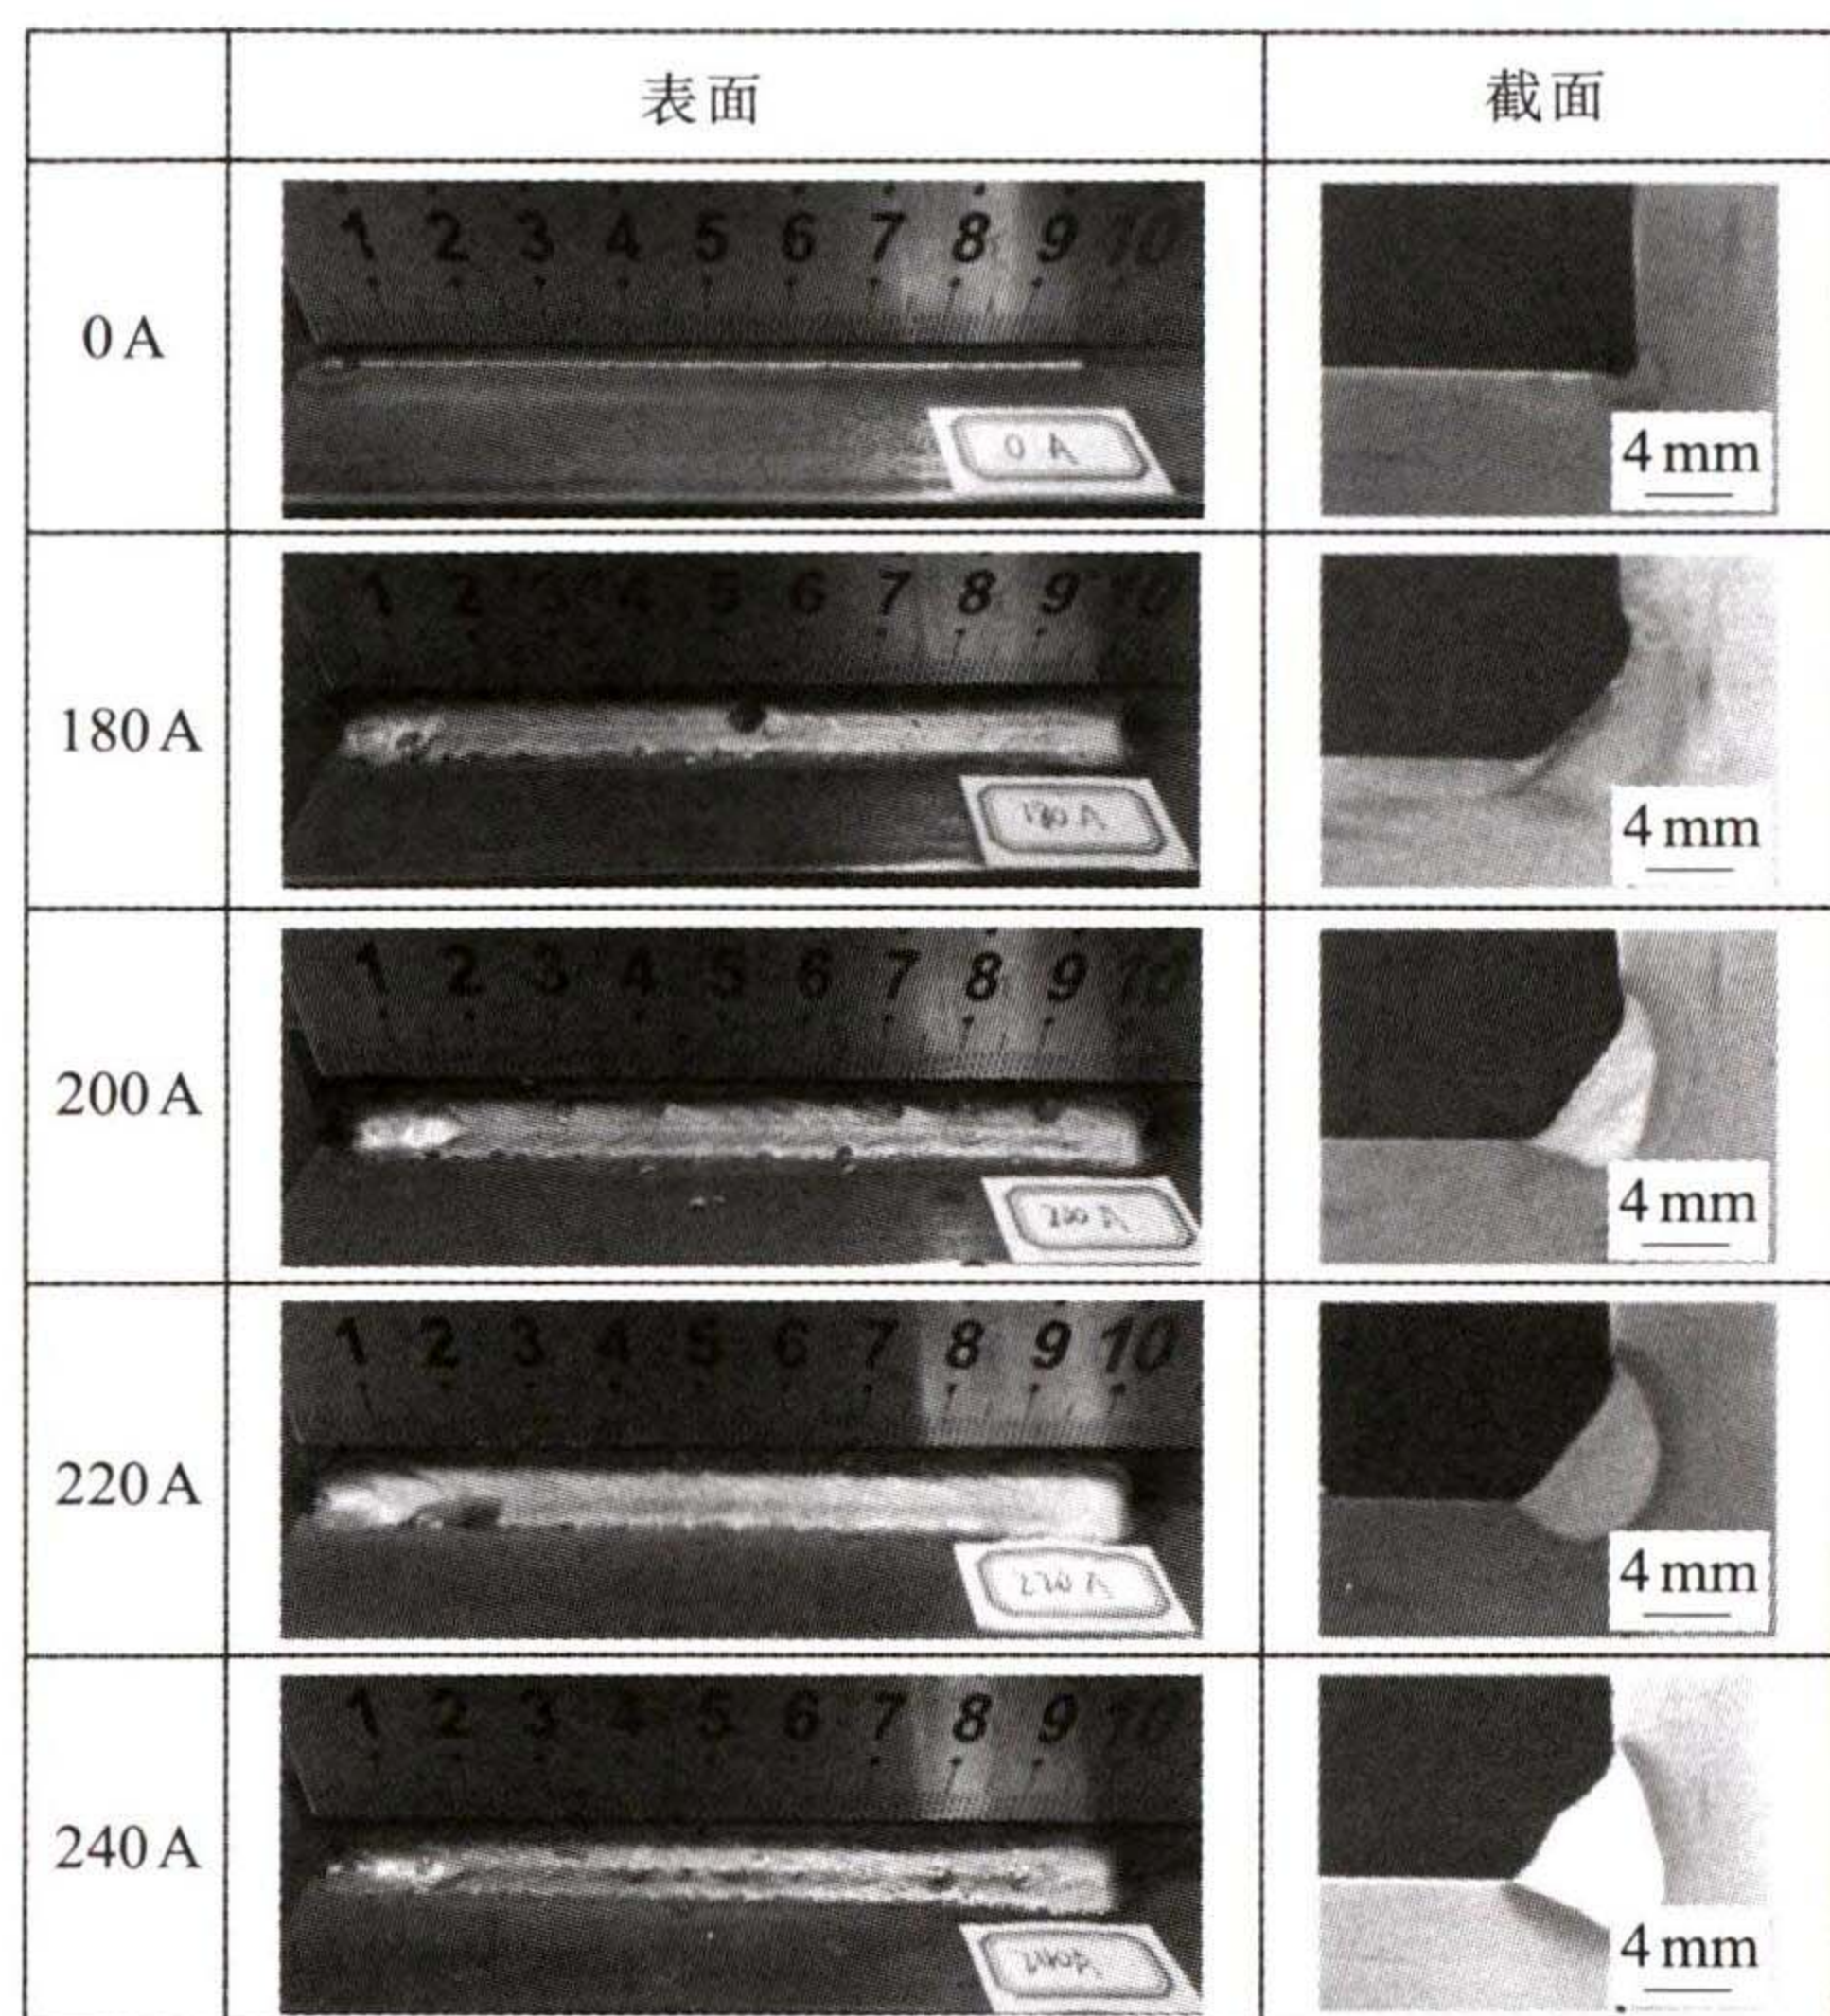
不同焊接电流下焊缝的表面和截面形貌
